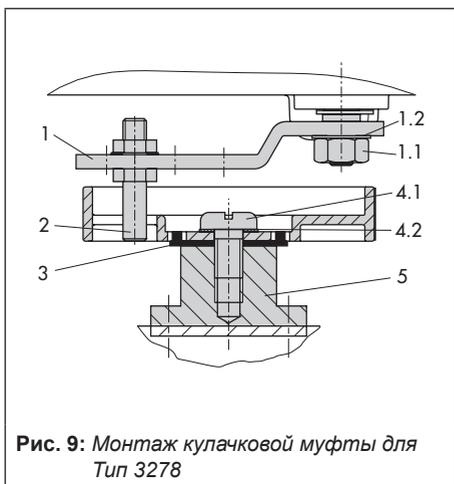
Монтаж кулачковой муфты для Тип 3278
